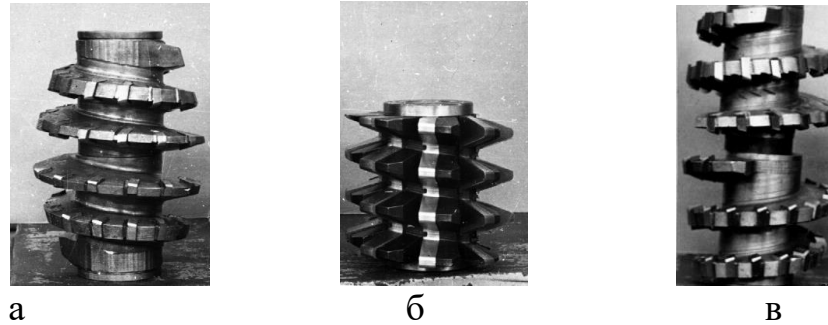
Експериментальний зубофрезерний інструмент:
